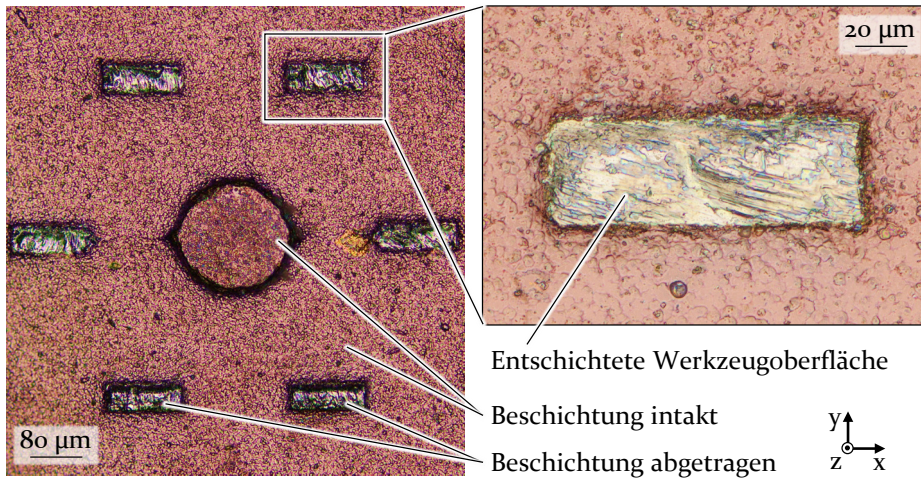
Mikroskopaufnahmen texturierter Werkzeuge mit Titanbeschichtung
